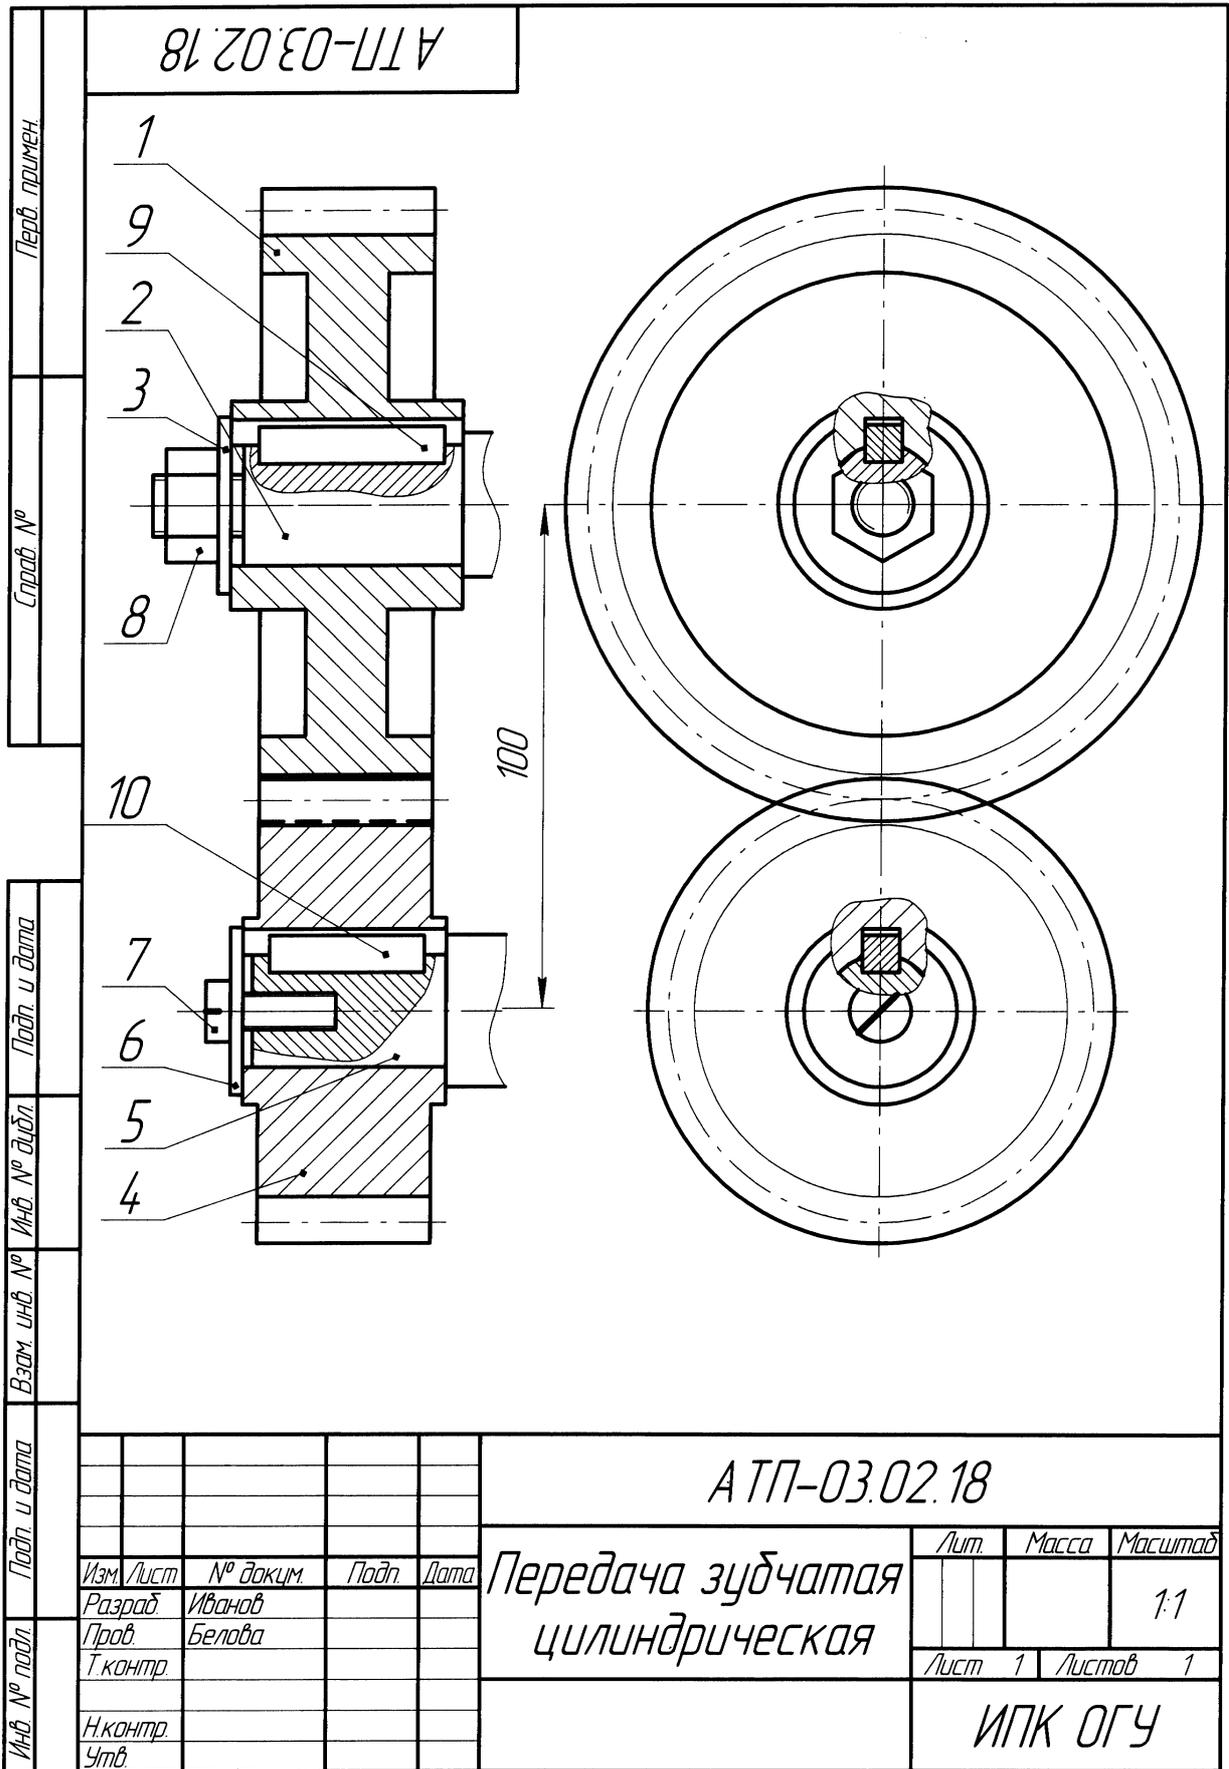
Пример изображения зубчатой цилиндрической передачи
